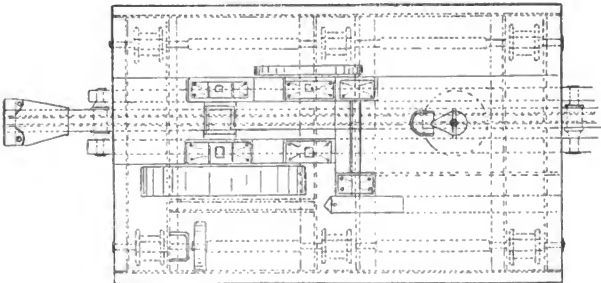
Koksandruckmaschine. Grundriss.
